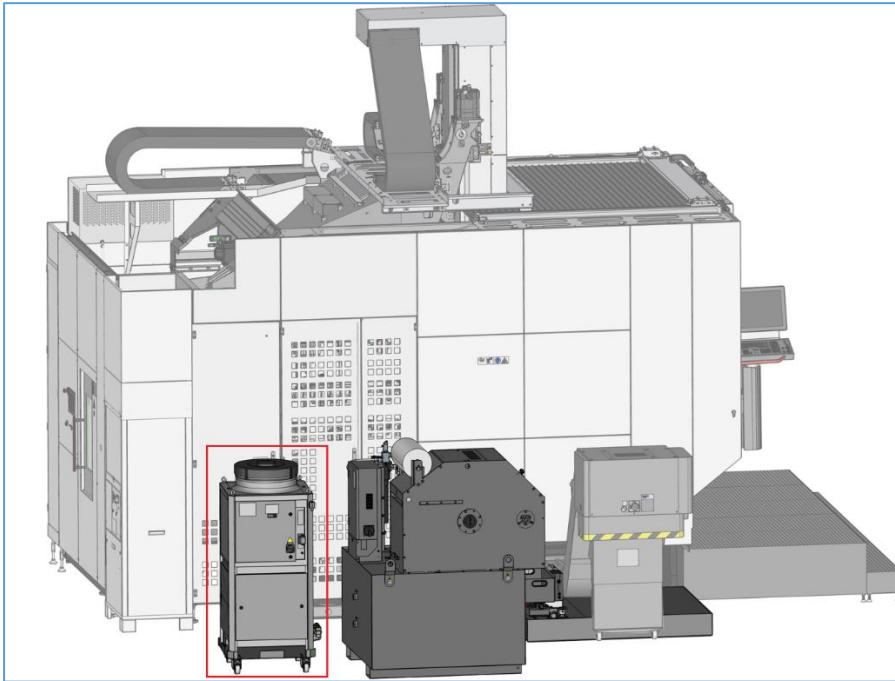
CNC-Werkzeugmaschine und einem Chiller (rot) für die Kühlung der Kühlschmierstoffes (Emulsion) in maschinennaher Aufstellung.
